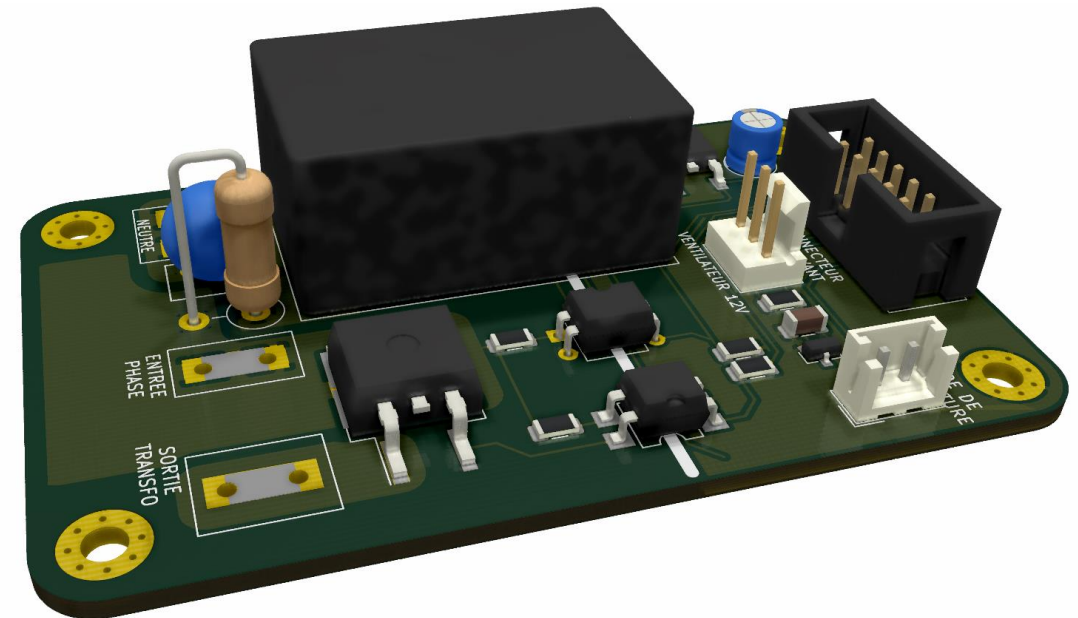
vue 3D de la carte de puissance de la soudeuse par point
